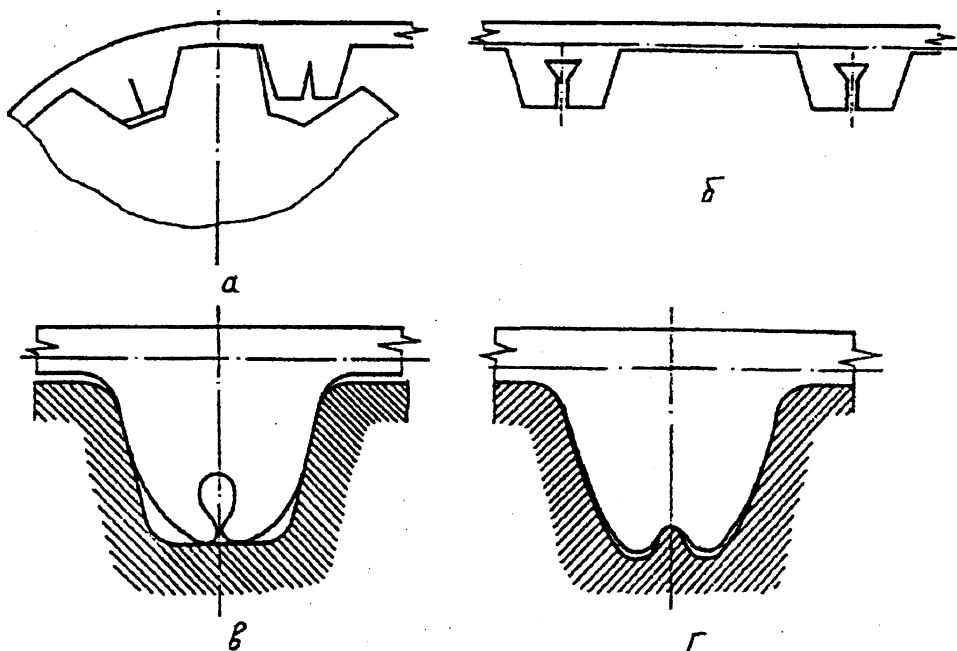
Конструкции зубчатых ремней с податливыми вершинами зубьев
